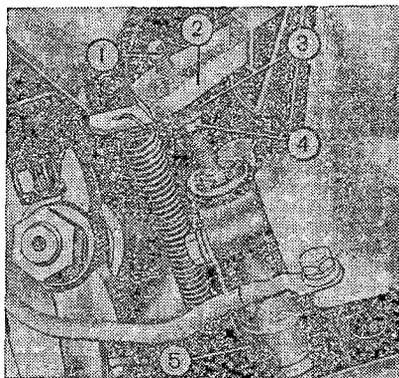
Рабочий цилиндр и вилка выключения сцепления:
